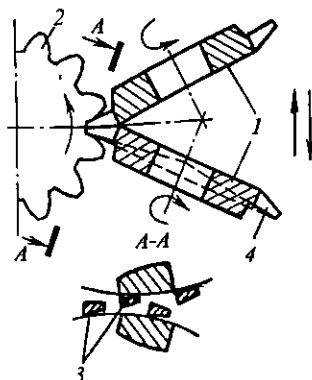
Схема нарезания зубьев прямозубых конических колес двумя дисковыми фрезами
